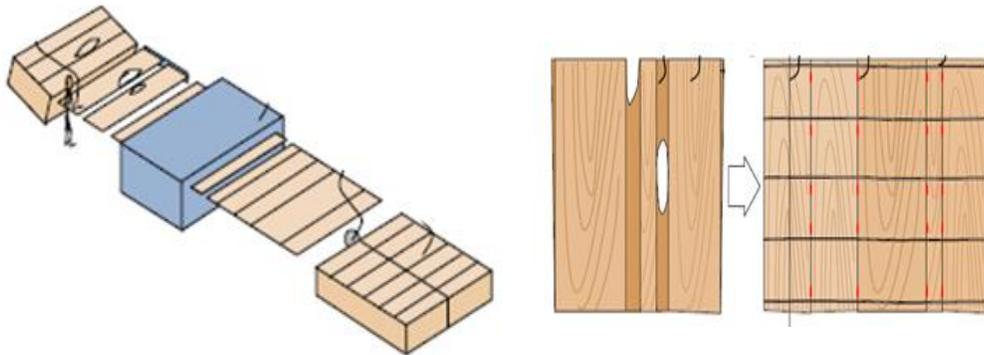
Muestra el proceso de ensamblado de chapas.
